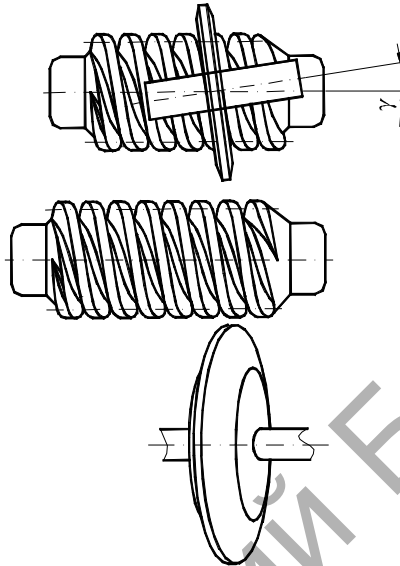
Скрещивающиеся оси червяка и инструмента [65]
